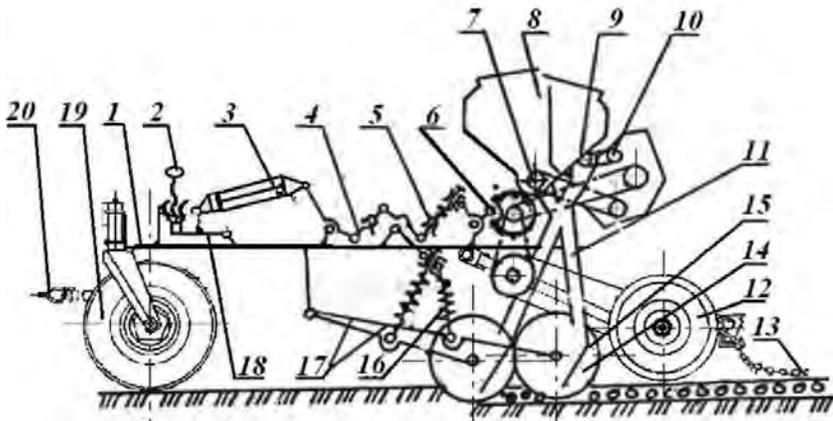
Схема зерновой прессовой сеялки СЗП-3,6А:
